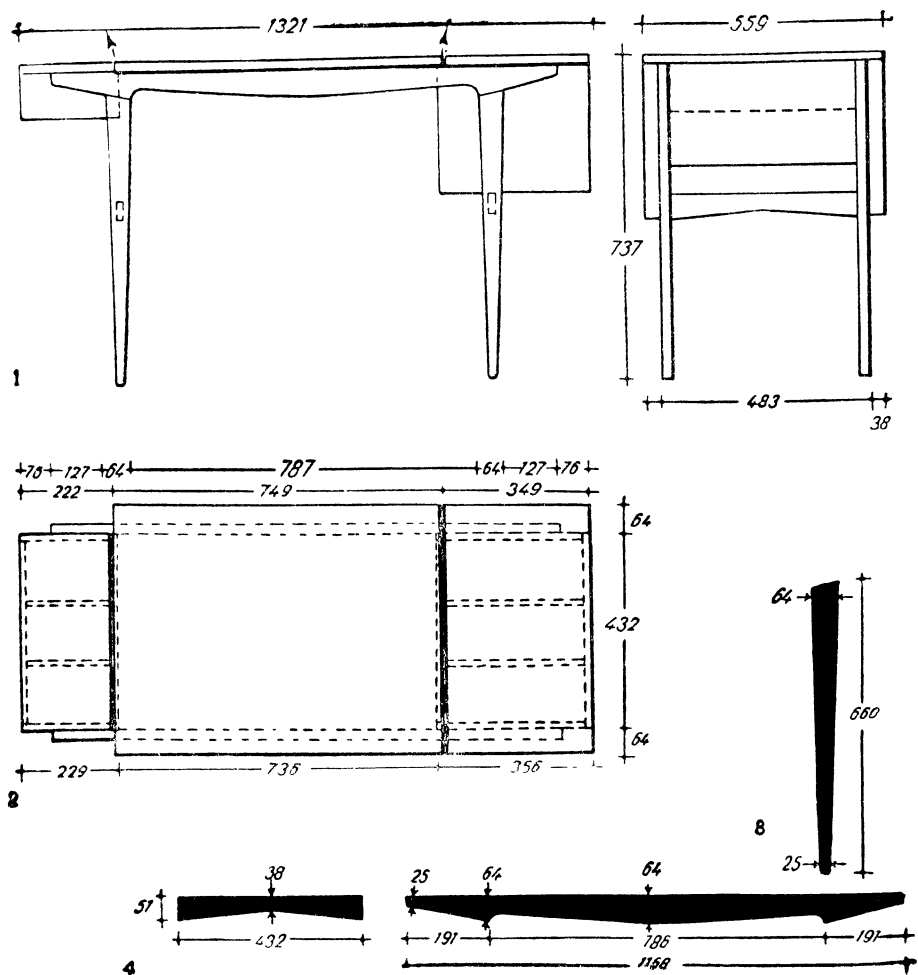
4. 1 — вид спереди и сбоку; 2 — вид сверху; 3 — ножка, 4 — сарги.
